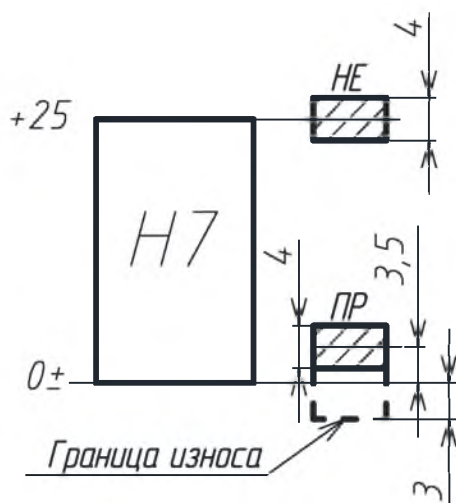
Схема расположения полей допусков рабочих калибров Ø40H7
